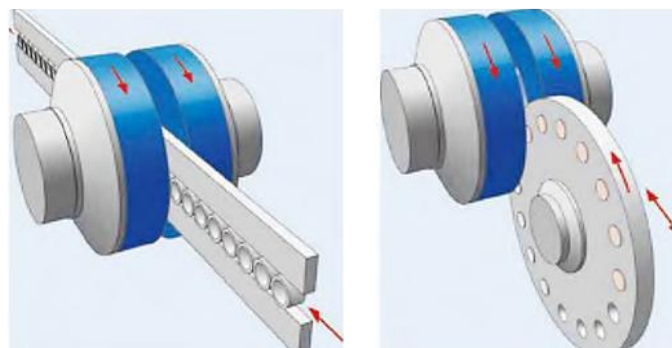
Схемы использования процесса плоского торцевого шлифования сдвоенными шлифовальными кругами
